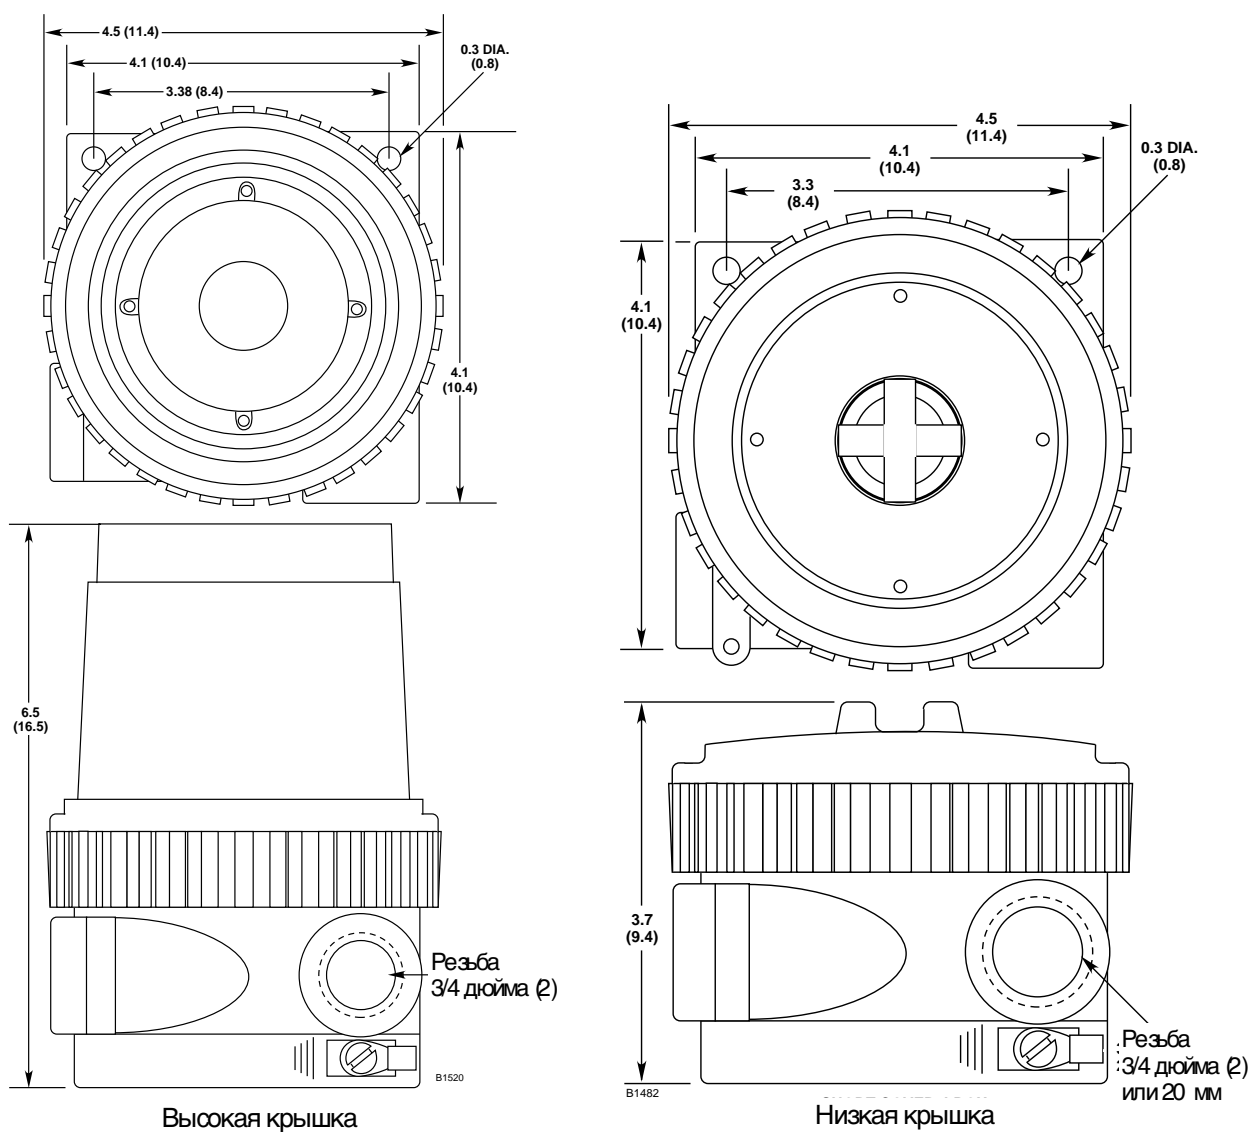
Габаритные размеры соединительной коробки в дюймах (мм).
